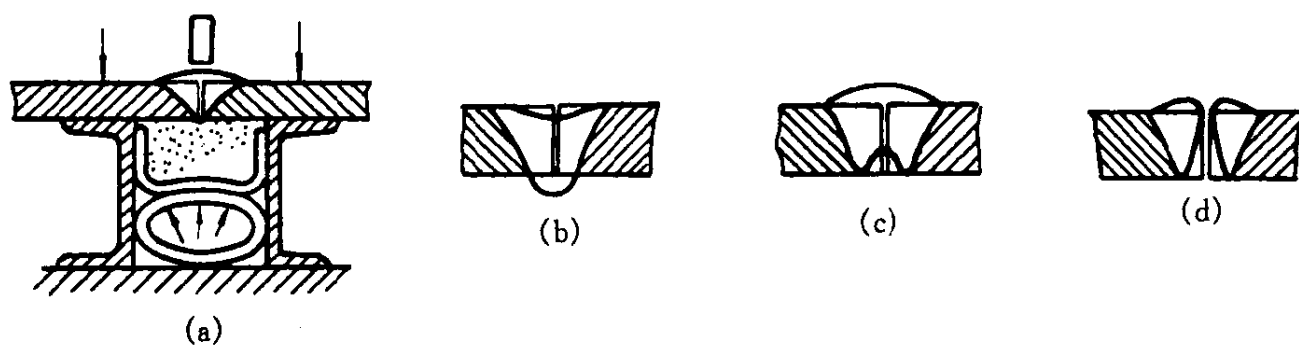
带焊剂垫的对接焊缝的焊接
